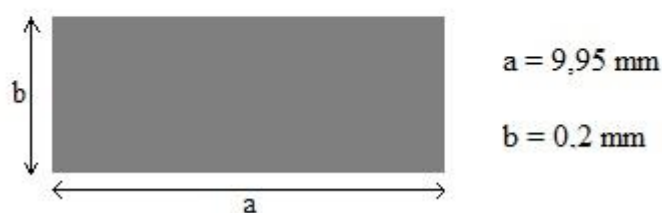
Dimensões da superfície da placa que entra em contato com a amostra
